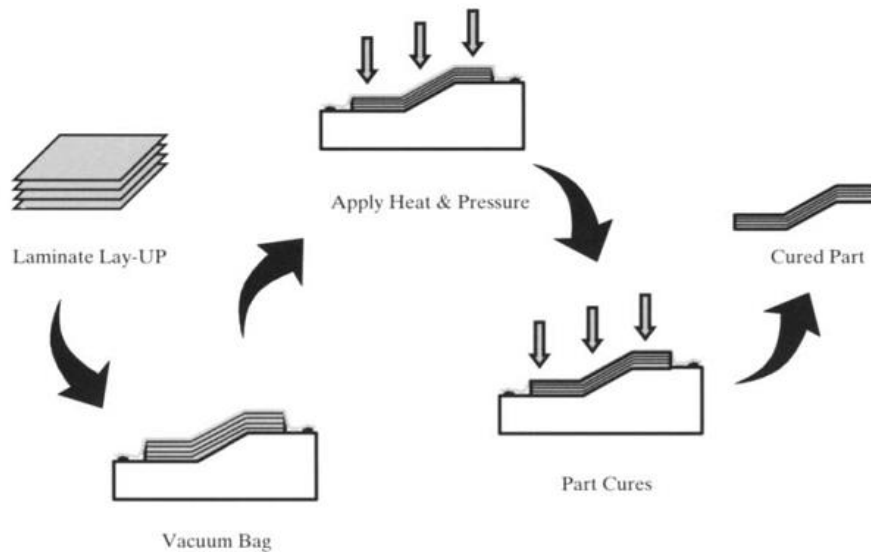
Representação esquemática do processo de Moldação por Saco de Vácuo [26].
